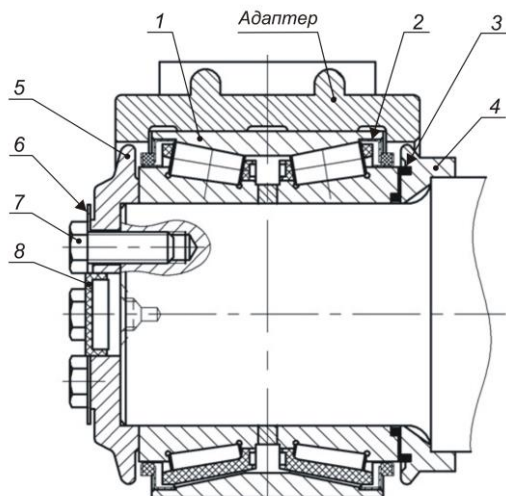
Конический подшипниковый узел с адаптером с базовыми подшипниками в габаритных размерах 130×230×150, 130×250×160 и 150×250×160 мм марки SKF:
